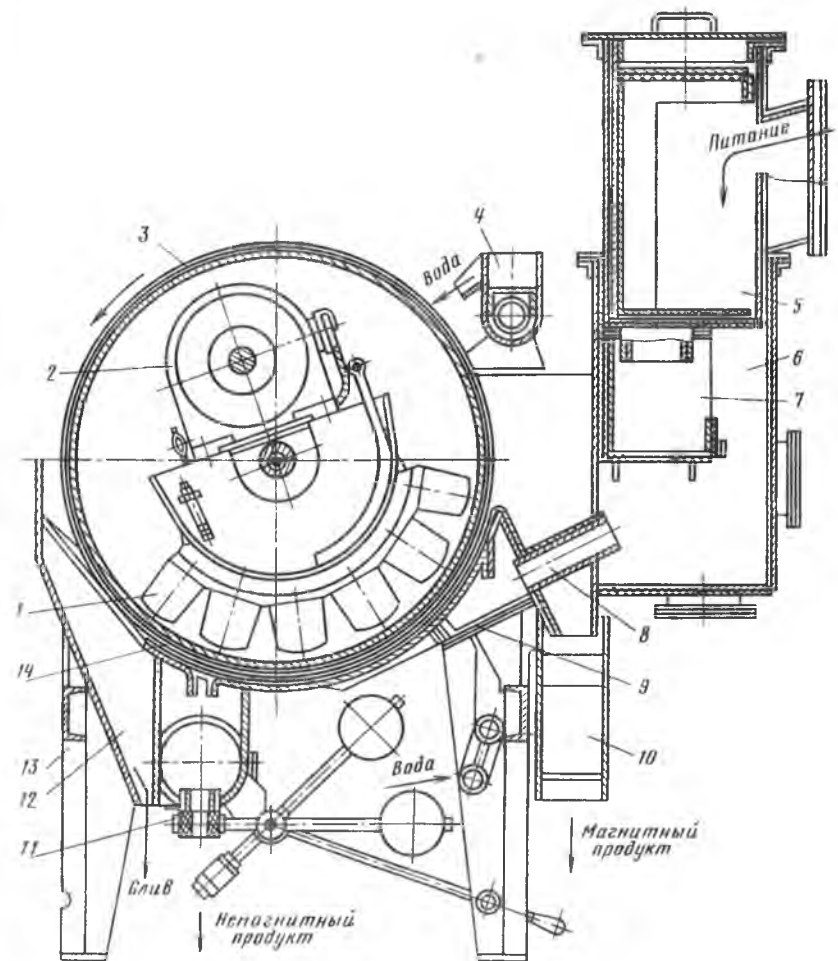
Барабанный магнитный сепаратор 209-СЭ с противоточной ванной:
